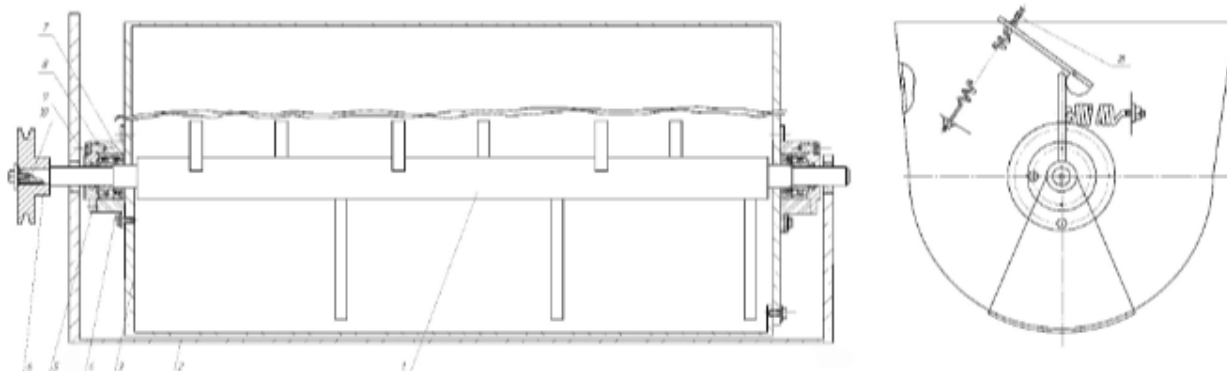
Дозуючий пристрій очисника вороху ОВС-25: 1- активатор; 2 – корпус; 3 – заслінка; 4, 8 – підшипник; 5 – кришка; 6 – шків; 7, 9 – ущільнення; шків; 10 - двоплечій важіль; 11,12 – пружина.
